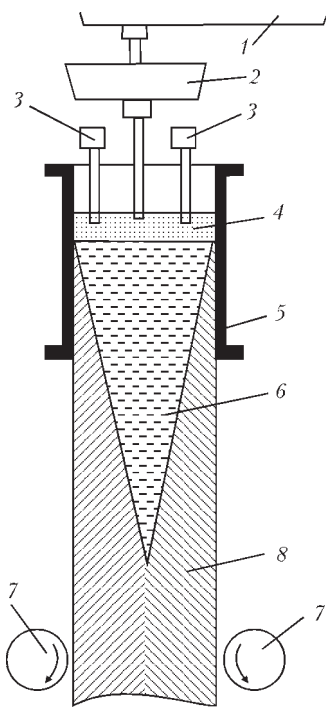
Схема непрерывной разливки стали в сочетании с электрошлаковым обогревом мениска разливаемого металла в кристаллизаторе МНЛЗ: 1 — сталеразливочный ковш; 2 — промежуточный ковш; 3 — нерасходуемые электроды; 4 — шлаковая ванна; 5 — кристаллизатор; 6 — жидкий металл; 7 — тянущие валки; 8 — заготовка
